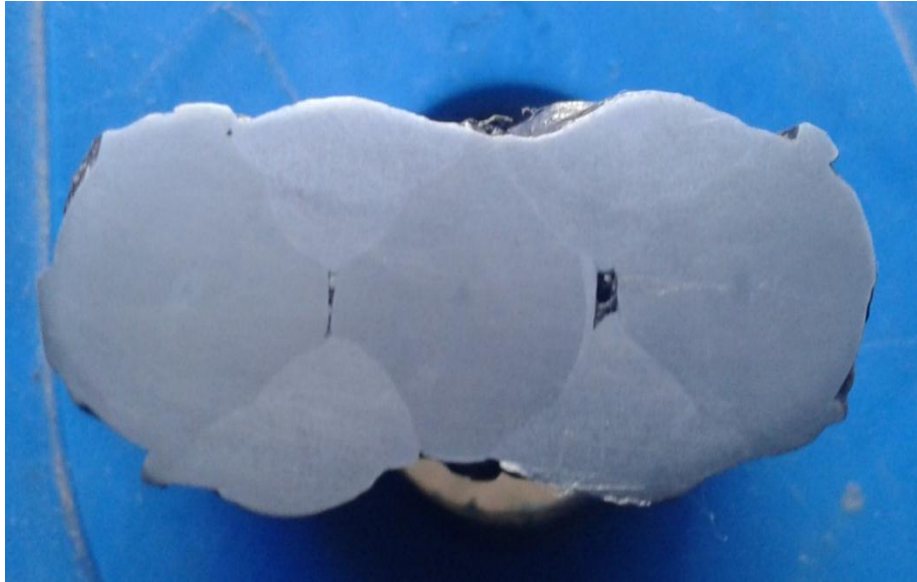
Soldado a tope indirecto, vemos la inclusión de escoria
